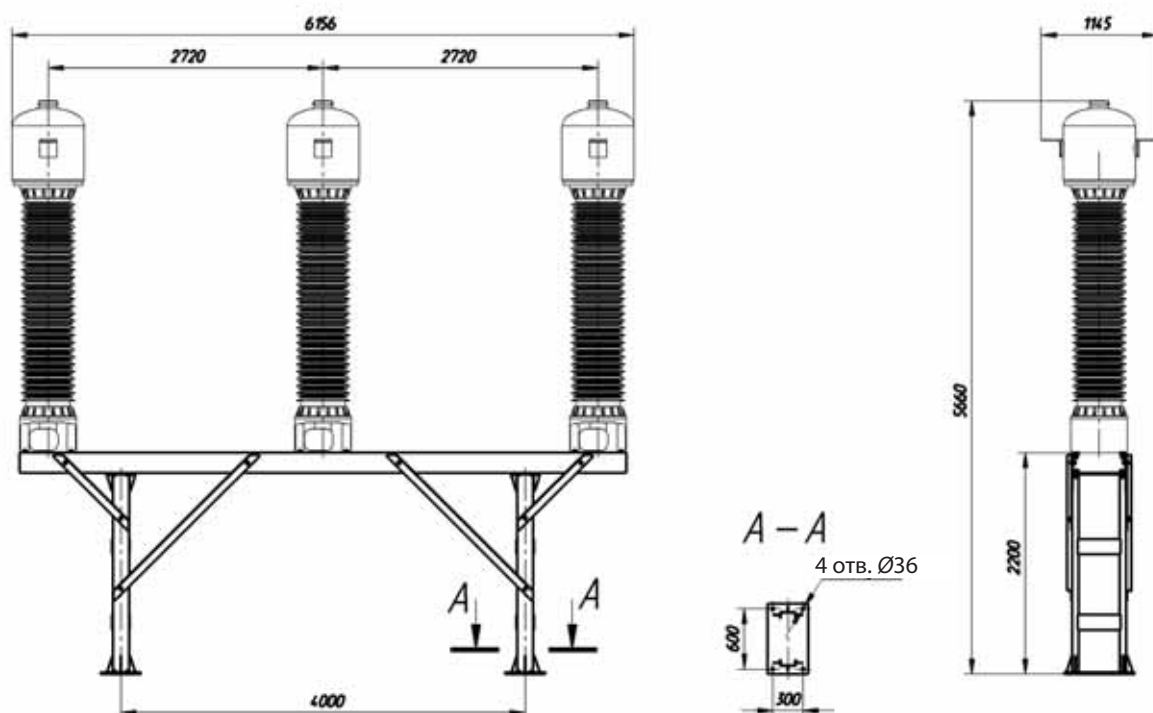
Установка блока трансформаторов тока ТРГ-220 на заводской металлоконструкции с покрытием горячим цинком
